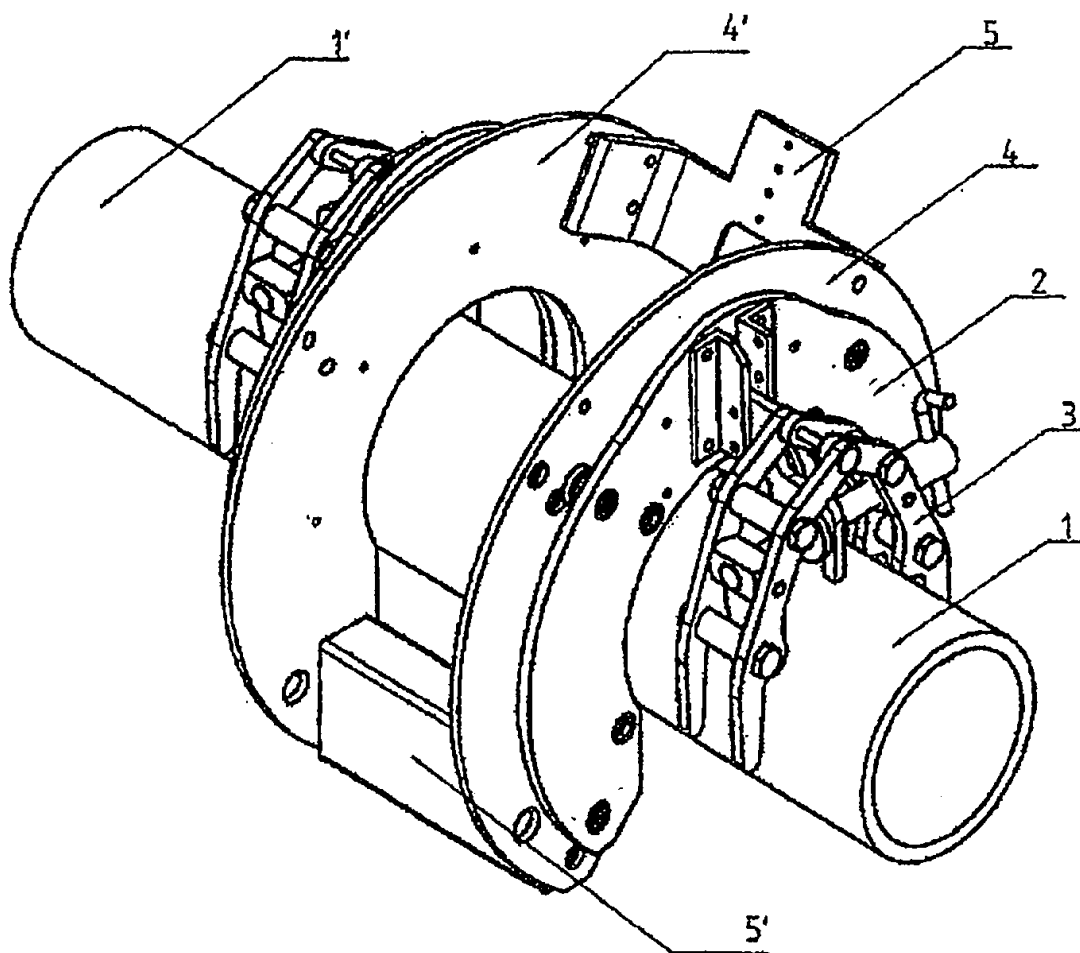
Устройство для соединения концов стальных труб орбитальной сваркой:
